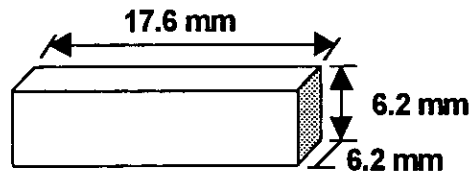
Dimensiones del bloque rectangular para la prueba mecánica de compresión.
